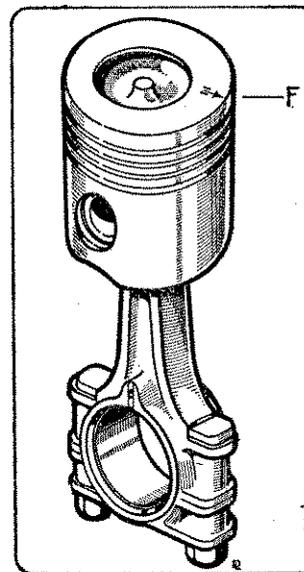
RIFERIMENTO MONTAGGIO PISTONE.
